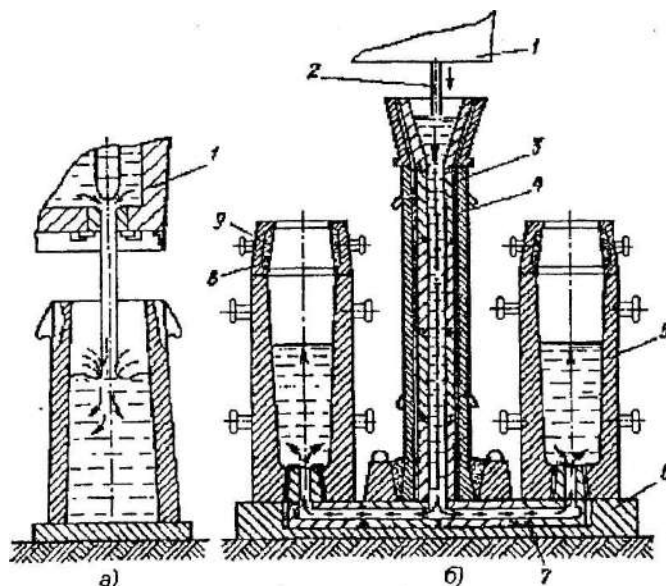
Разливка стали в изложницы: а - сверху; б – сифоном
